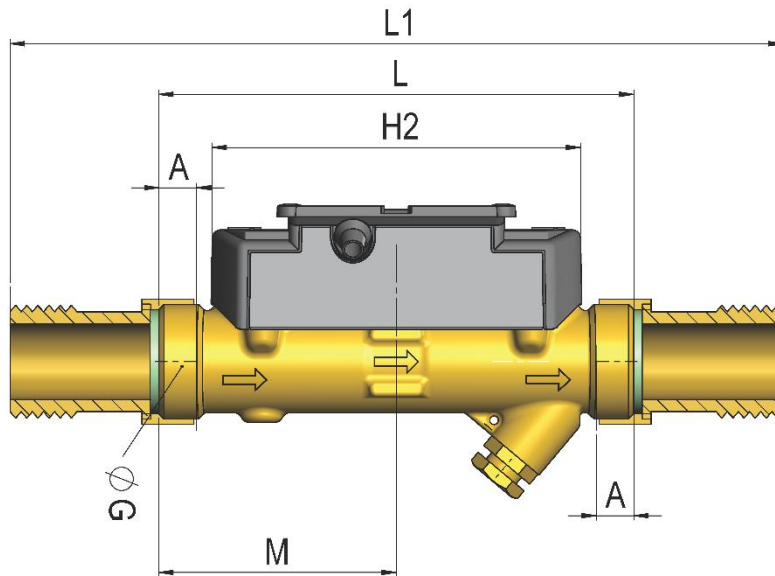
Maßskizzen für ULTRAFLOW® 54 Gewindezähler des Typs 65-5-XXHX-XXX mit Verschraubungen.
